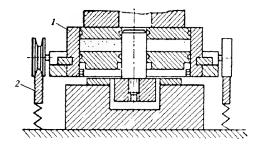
Схема прессования с подпрессовкой при подпружиненном рельсовом пути: I — тележка с пресс-формой; 2— подпружиненный рельсовый путь
